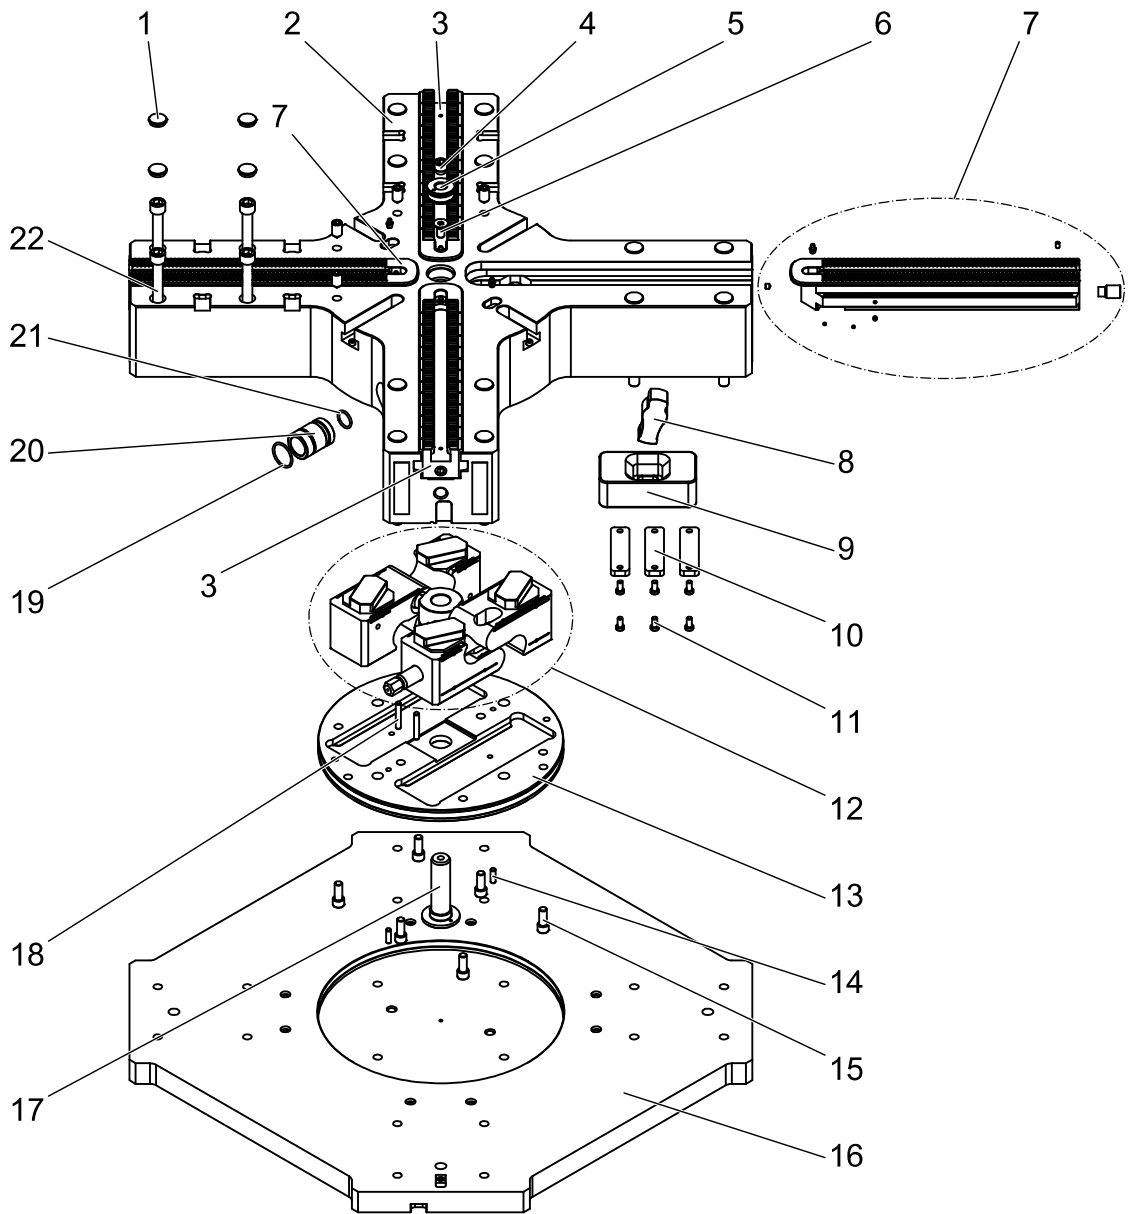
Smontaggio/montaggio del mandrino di serraggio
